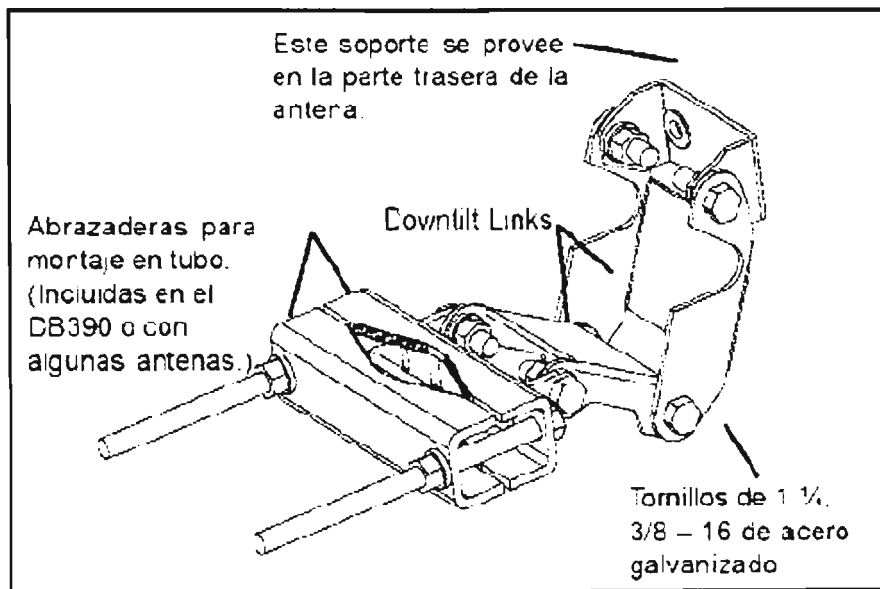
Parte superior del DB5098 ensamblado al tubo
